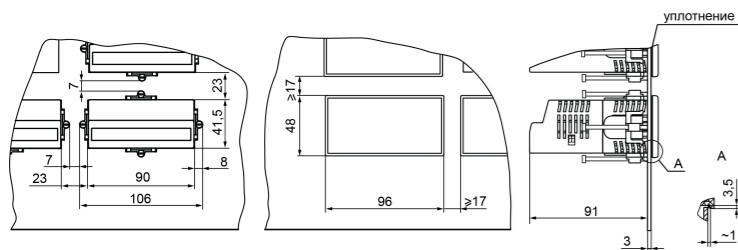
Корпус Щ2 в щите толщиной 3 мм
